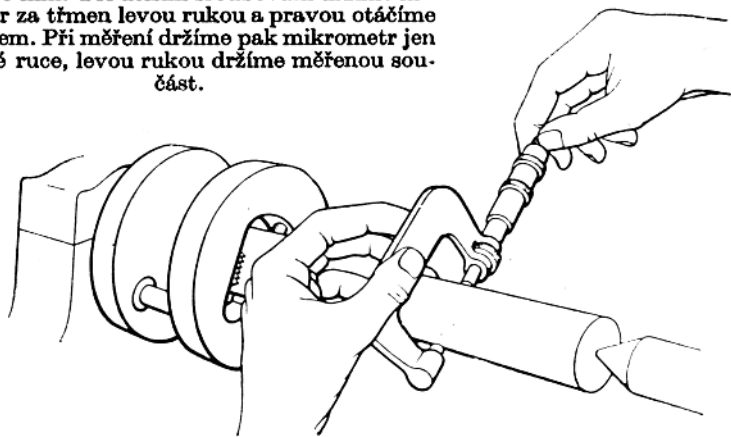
Měření větším mikrometrem pro rozměr 50 až 75 mm. Při delším šroubování držíme mikrometr za třmen levou rukou a pravou otáčíme bubínkem. Při měření držíme pak mikrometr jen v pravé ruce, levou rukou držíme měřenou součást.
